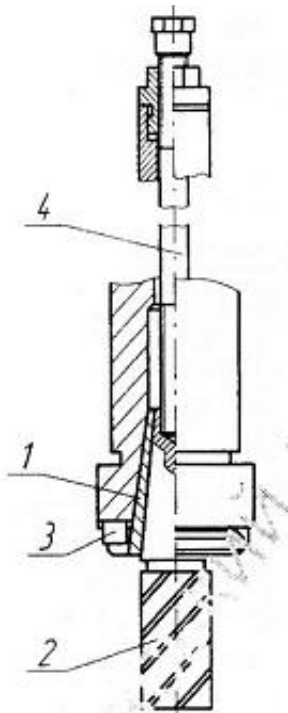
Схема закріплення фрези за допомогою перехідної втулки
